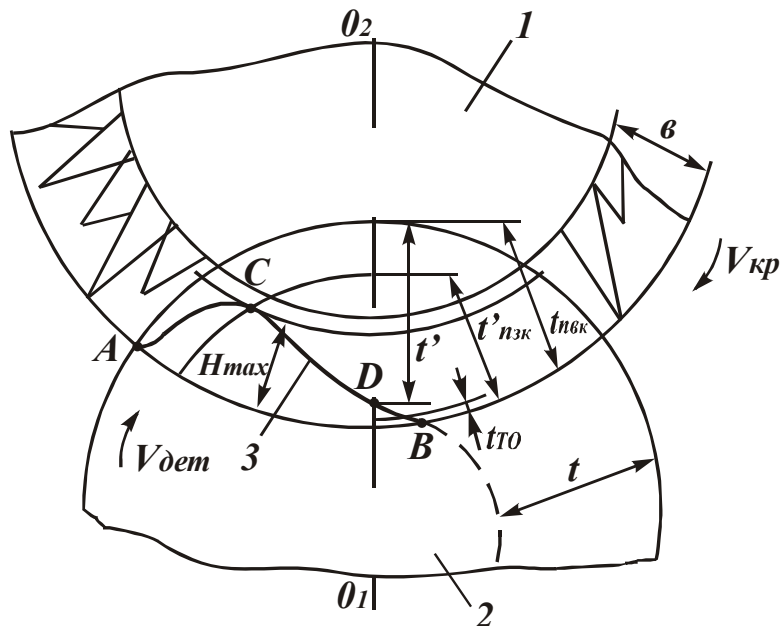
Изменение линии полного съема металла рабочей поверхности круга: 1 – круг; 2 – деталь; 3 – линия полного съема металла.
